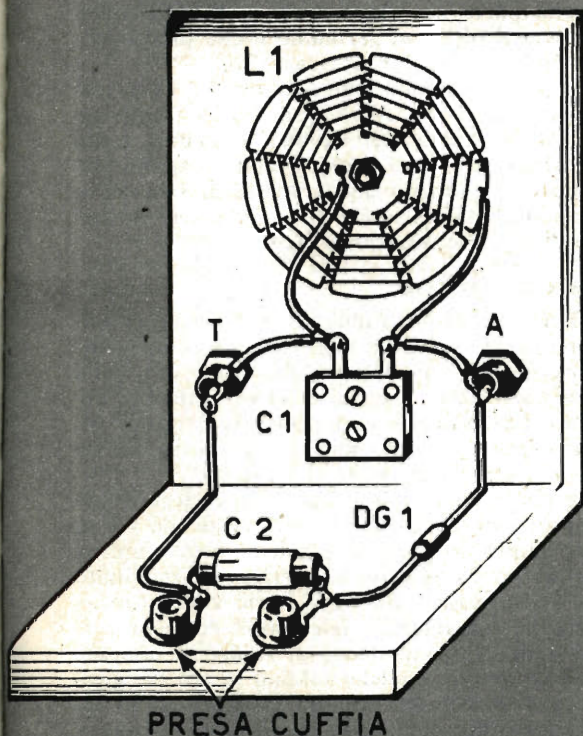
Il montaggio del ricevitore descritto nel testo e utilizzando la bobina a fondo di panierino può essere realizzato su due tavolette di legno unite ad angolo retto.
